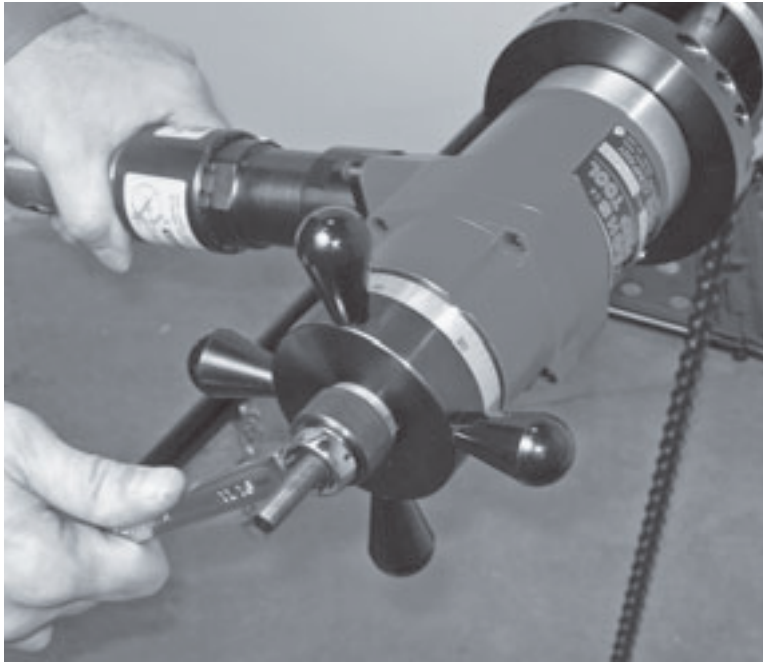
Halten Sie die Maschine in ihrer Position und ziehen Sie die Zugstangenmutter an.
